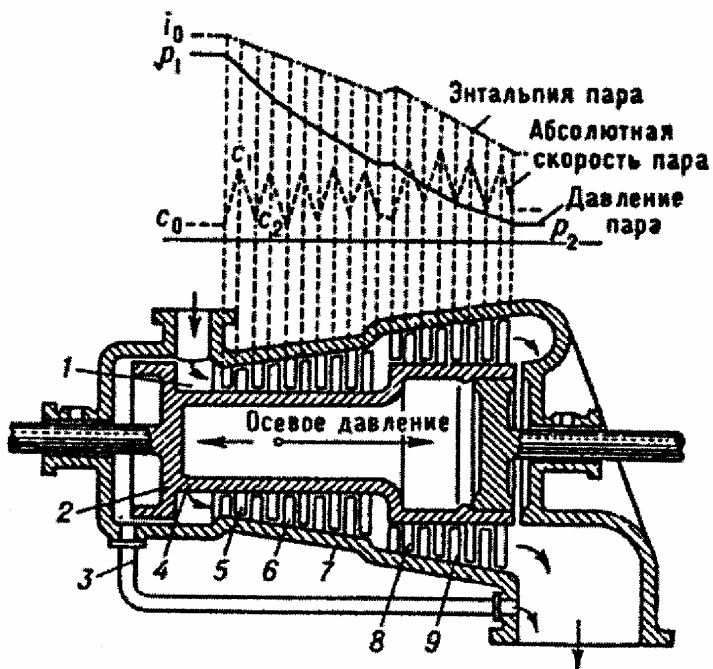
Схематический разрез небольшой реактивной турбины: 1 – кольцевая камера свежего пара; 2 – разгрузочный поршень; 3 – соединительный паропровод; 4 – барабан ротора; 5,8 – рабочие лопатки; 6,9 – направляющие лопатки; 7 – корпус.
